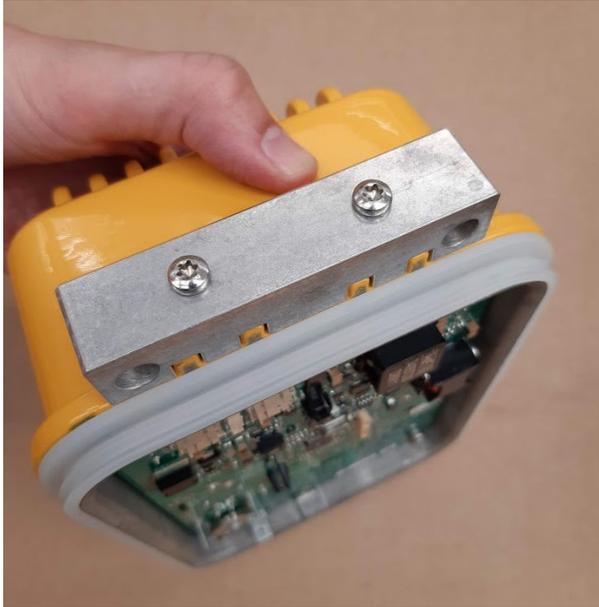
Montage bzw. Austausch des Schließblocks - Teil 1
